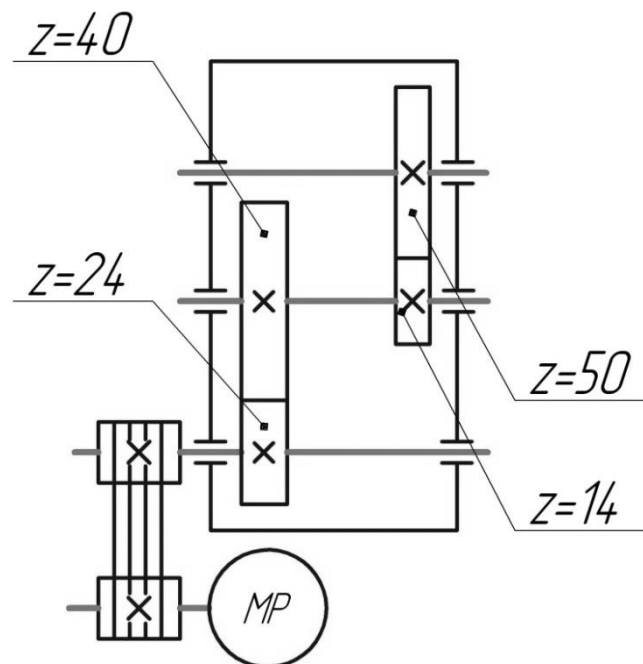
Кинематическая схема цилиндрического двухступенчатого редуктора
